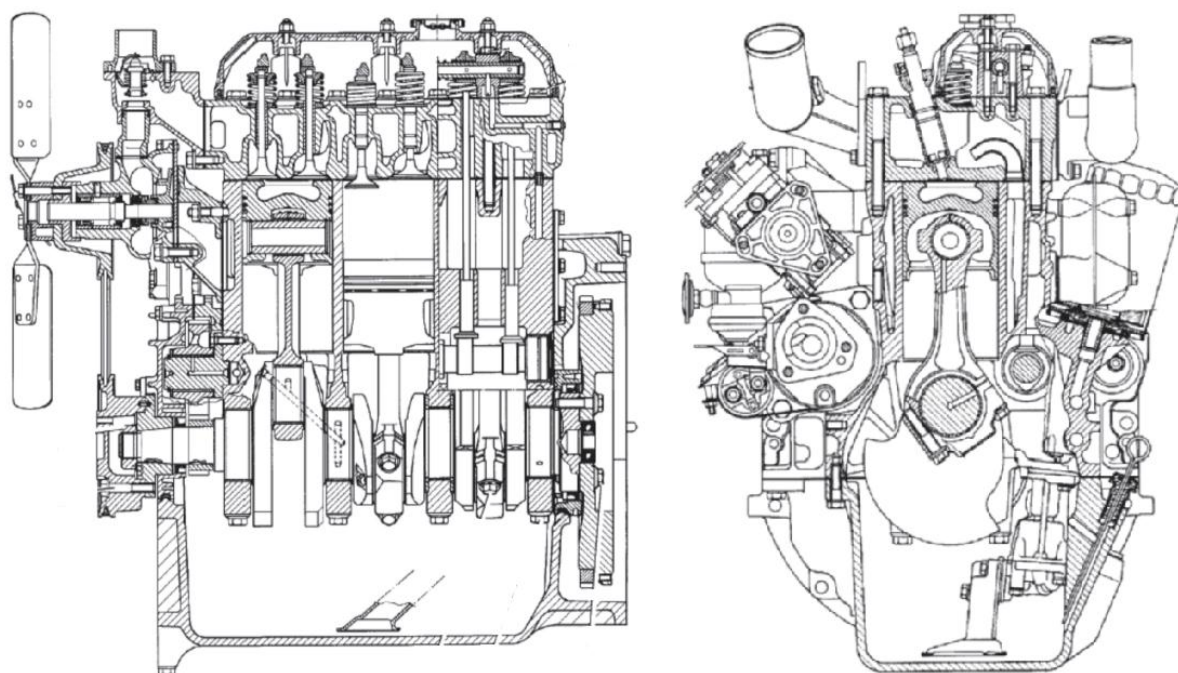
Vista em corte de um motor diesel 3 cilindros
